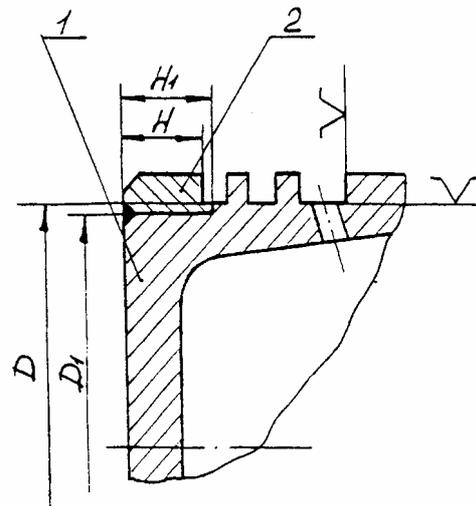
Схема установки ДРД при восстановлении канавки поршня: 1 – восстанавливаемая деталь, 2 – ДРД; D – диаметр канавки; D_1 – диаметр проточки; H – расстояние от канавки до днища; H_1 – длина проточки
